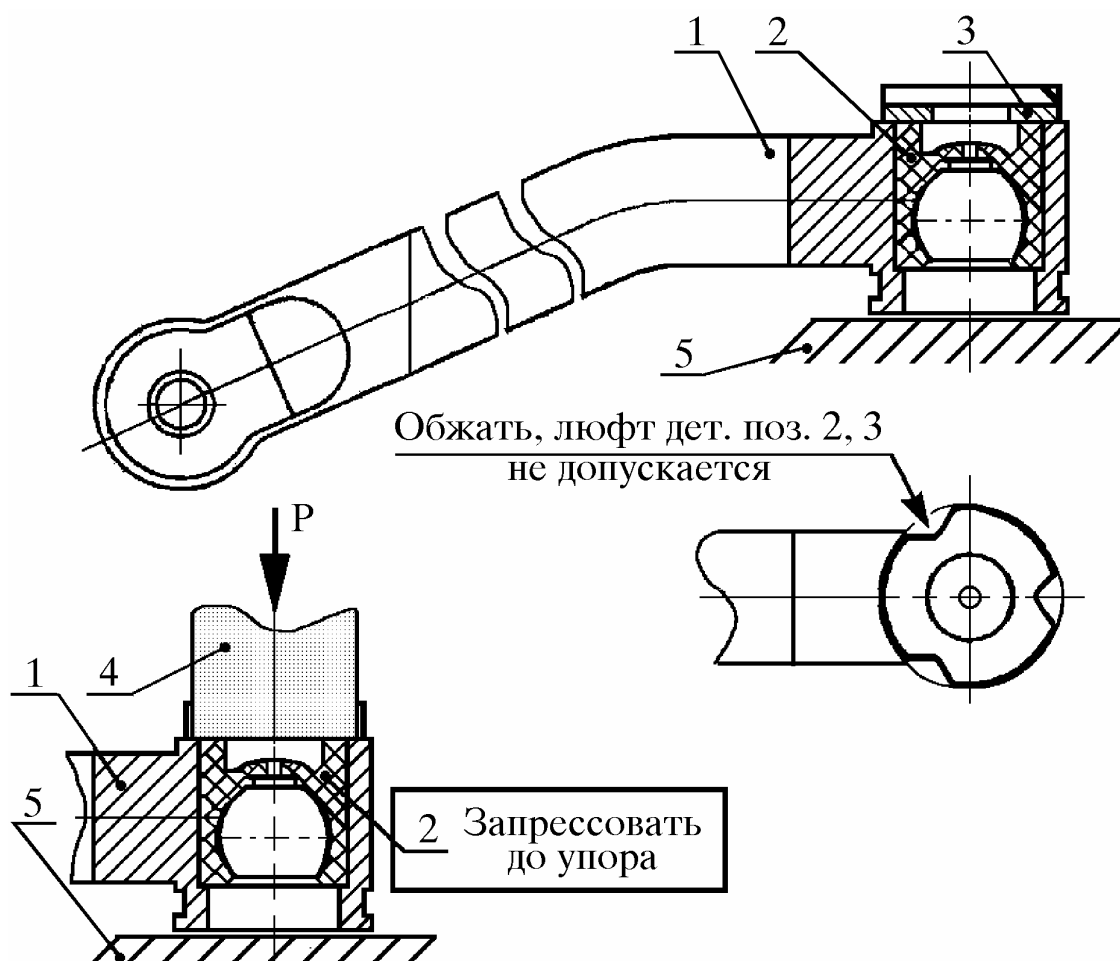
Сборка тяги управления с вкладышем, дет. 3111-1703029СБ:
